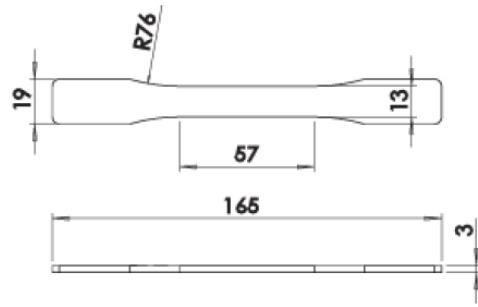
Dimensions de la proveta ASTM standard D638 Type I.
